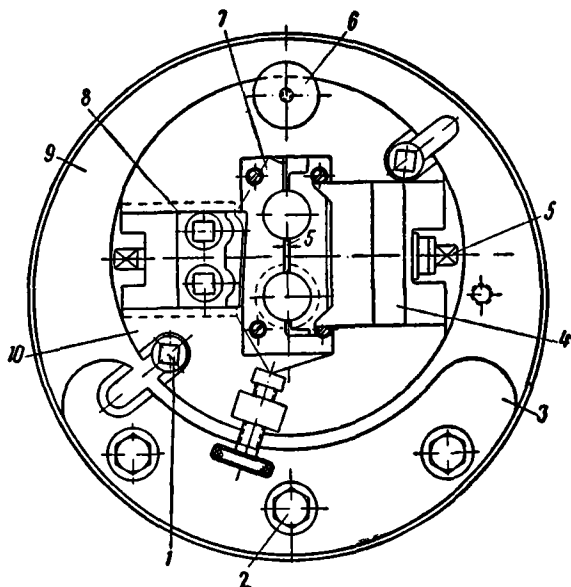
Приспособление для расточки отверстий в корпусе кронштейна щеткодержателя тягового двигателя НБ-412М:
